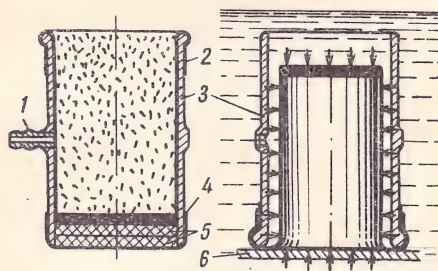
Формы для гидростатического прессования цилиндрических заготовок:
